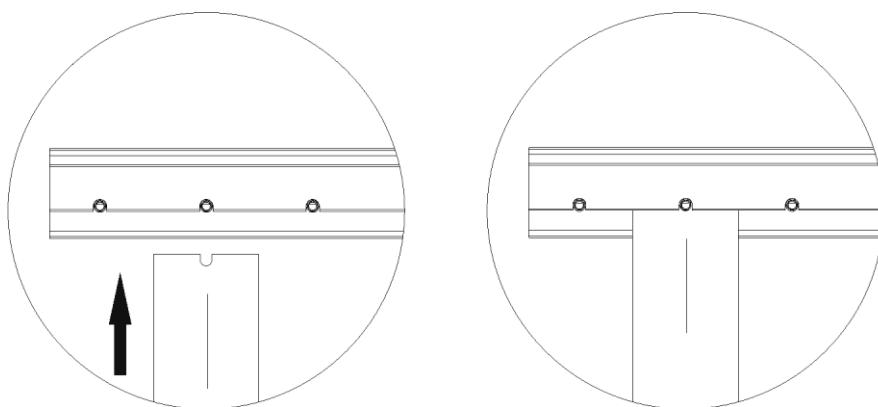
Образец установки соединительной панели, исполнение "моно"
